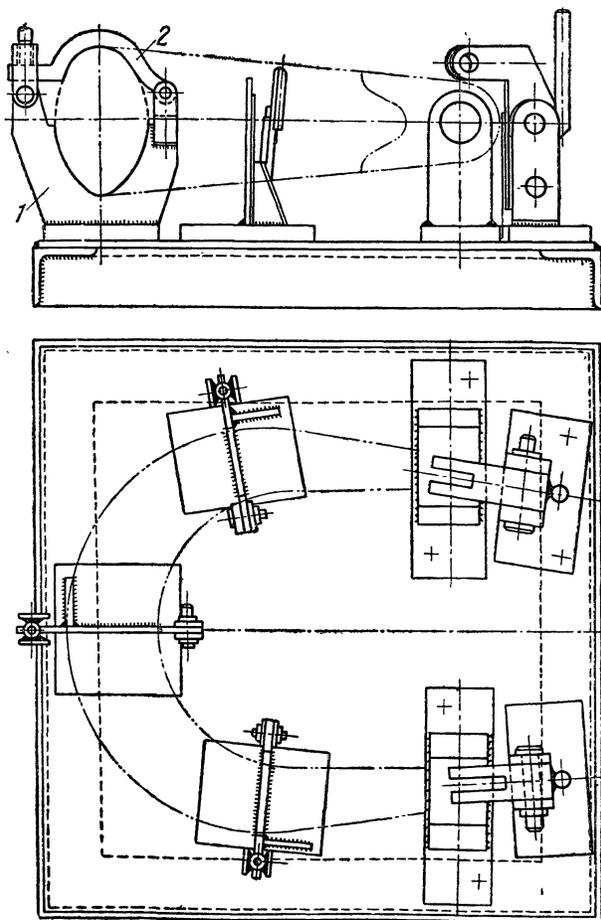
Приспособление для сборки, прихватки и торцовки патрубков.
